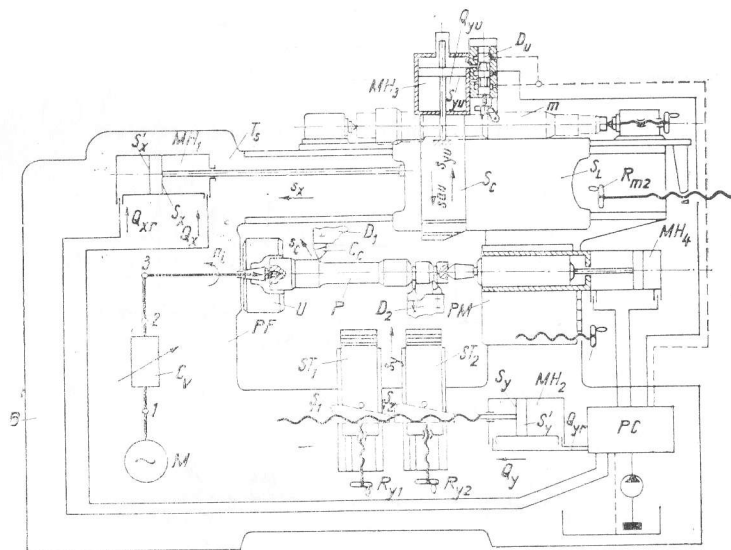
Schema cinematică principală a strungului de copiere.
